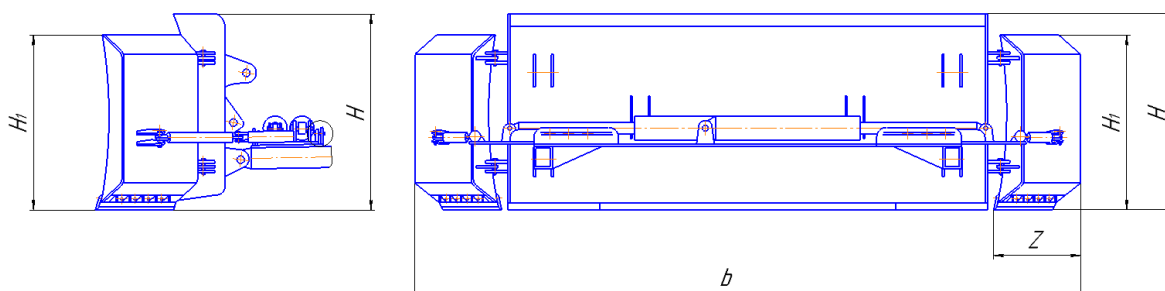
Параметры предлагаемой конструкции рабочего органа
